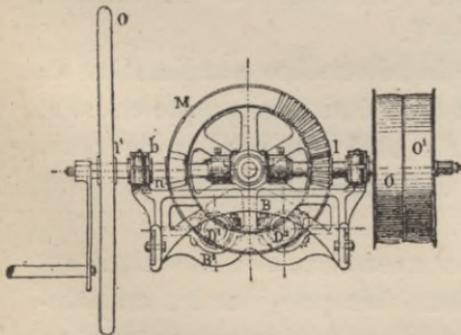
Projection d'arrière en avant des mécanismes de mouvement (perpendiculaire aux axes).
